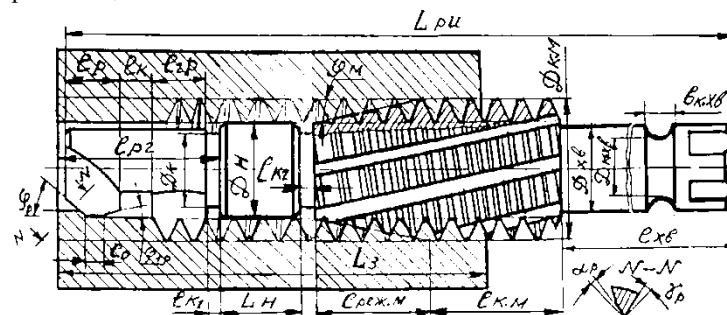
Схема, характеризующая способ нарезания внутренней резьбы комбинированным инструментом «Резец-гребёнка-метчик с направляющей»
